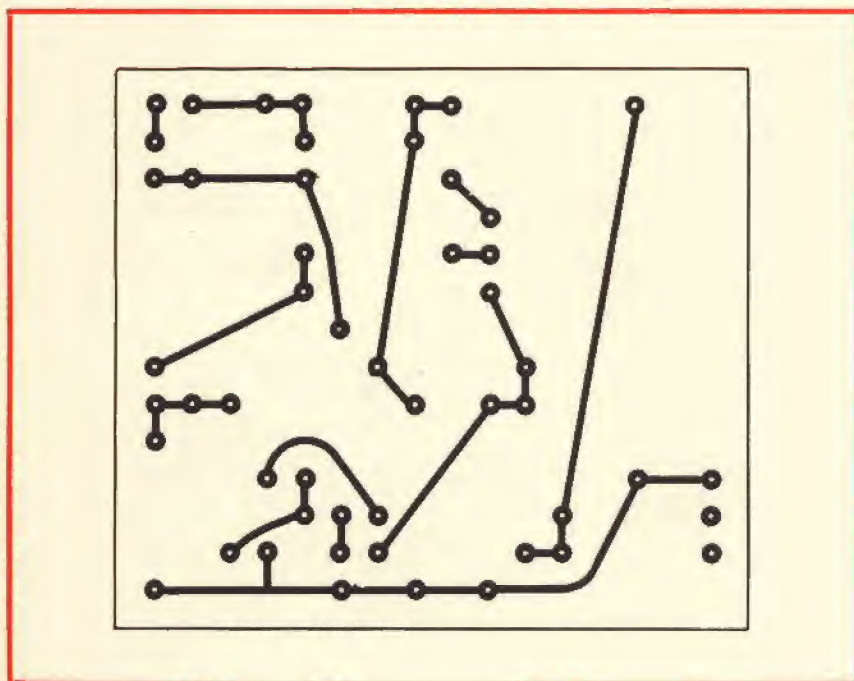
Piastrina di bachelite relativa al montaggio di figura 2 vista dal lato dei collegamenti.
